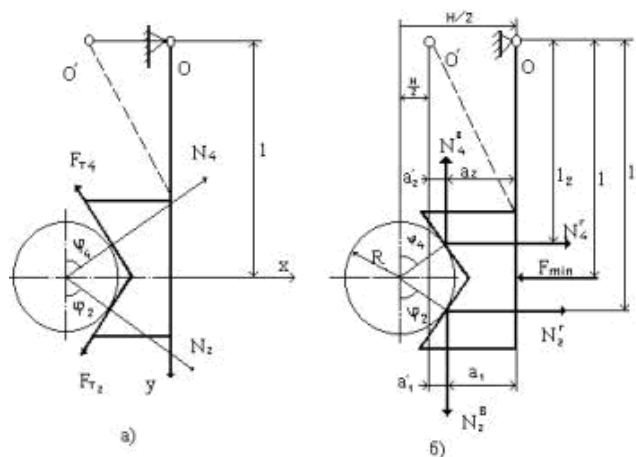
Розрахункова схема визначення зусиль схвата
